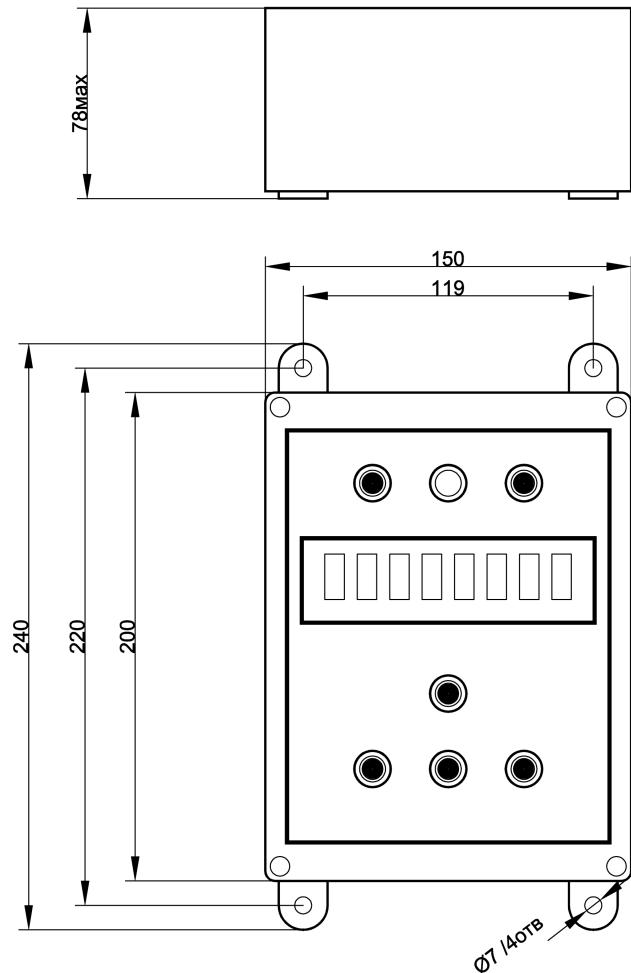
Габаритные и присоединительные размеры блока логики БЛ4-М.
